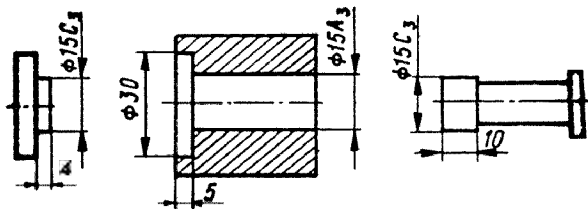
Разъемная форма для получения заготовки аншлифа
